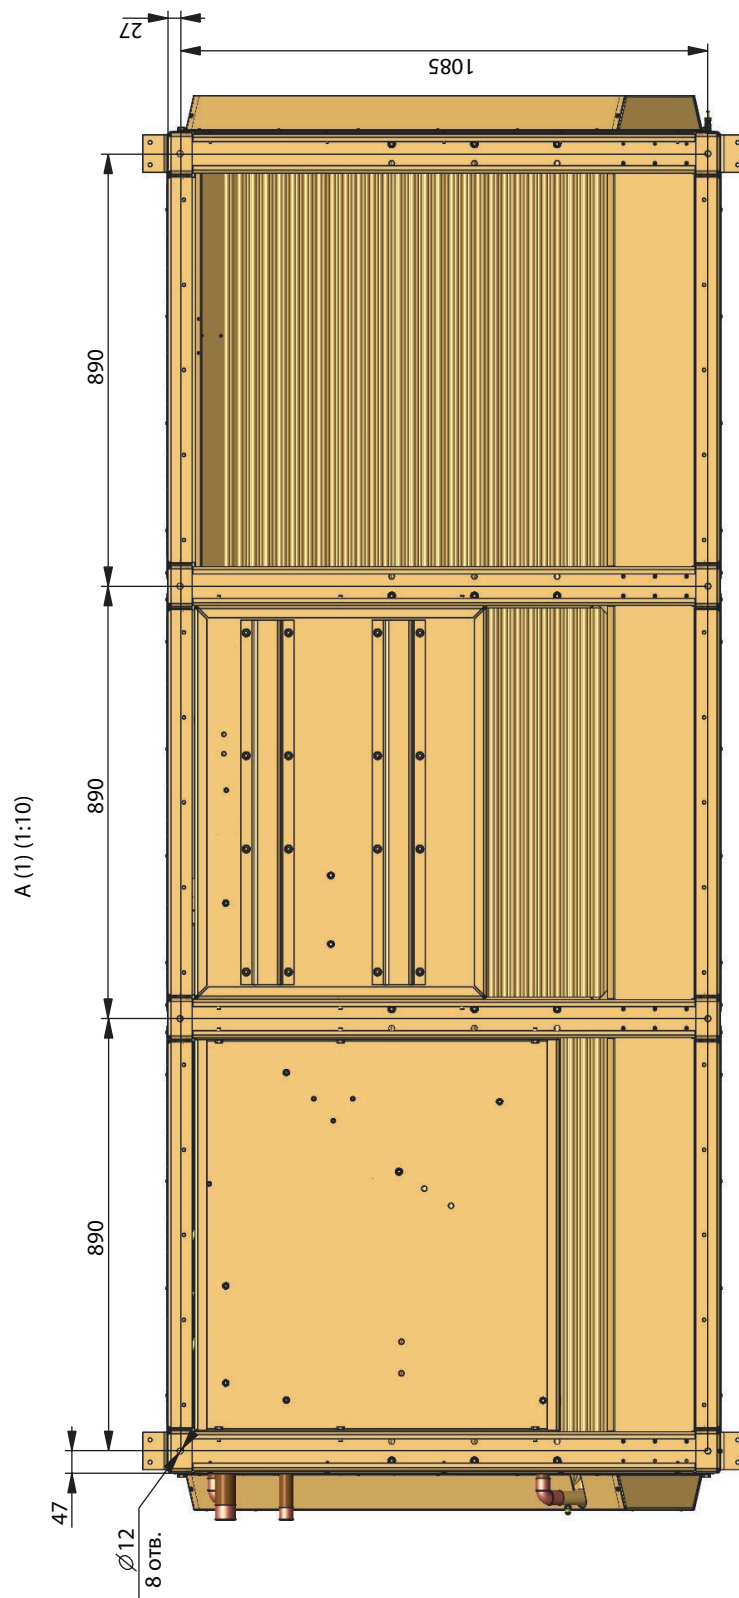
Агрегат компрессорный МАКК 120-951
